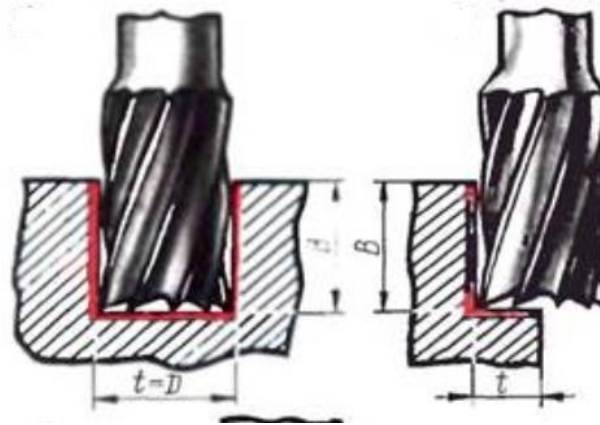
Схема обробки кінцевою фрезою [4, 282]
